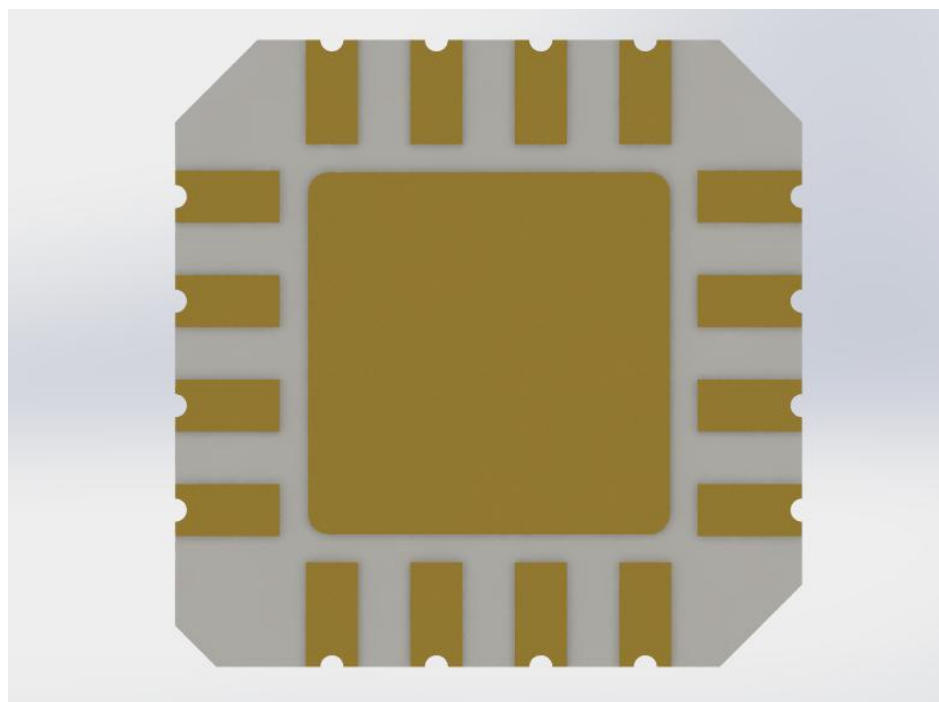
Корпус МИС Micran MP502 (вид снизу)
